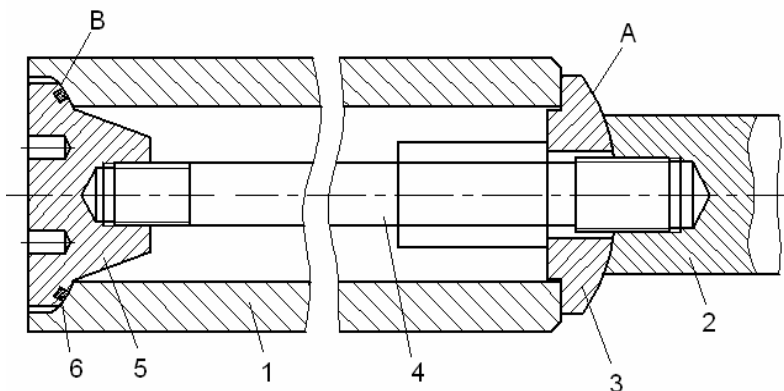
Рекомендуемая конструкция плунжера нефтепромыслового насоса: 1-плунжер; 2-шток; 3-шайба; 4-тяги; 5- заглушка; 6-уплотнитель
